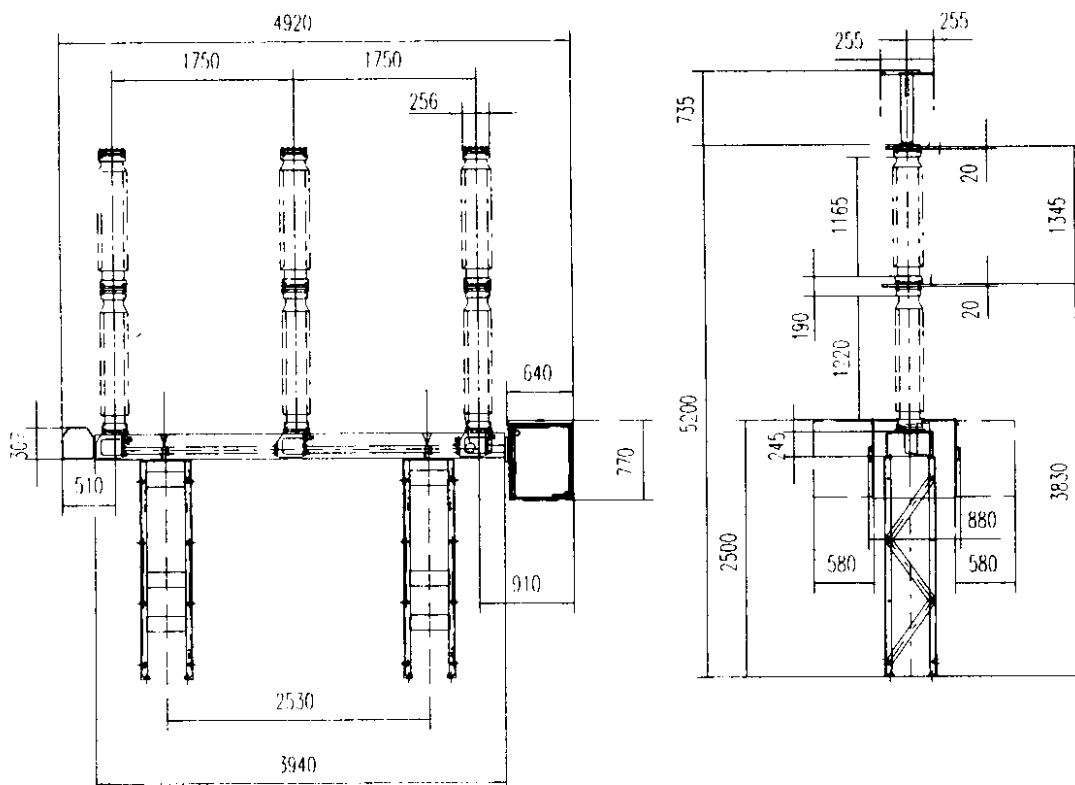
Внешний вид и габаритные размеры выключателя
